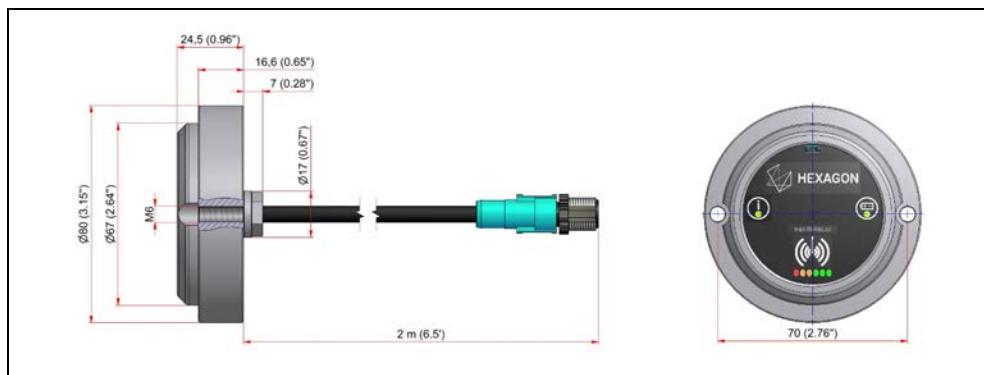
Abmessungen RWR95.50-A-PLUG-8 (Kabelabgang axial)
